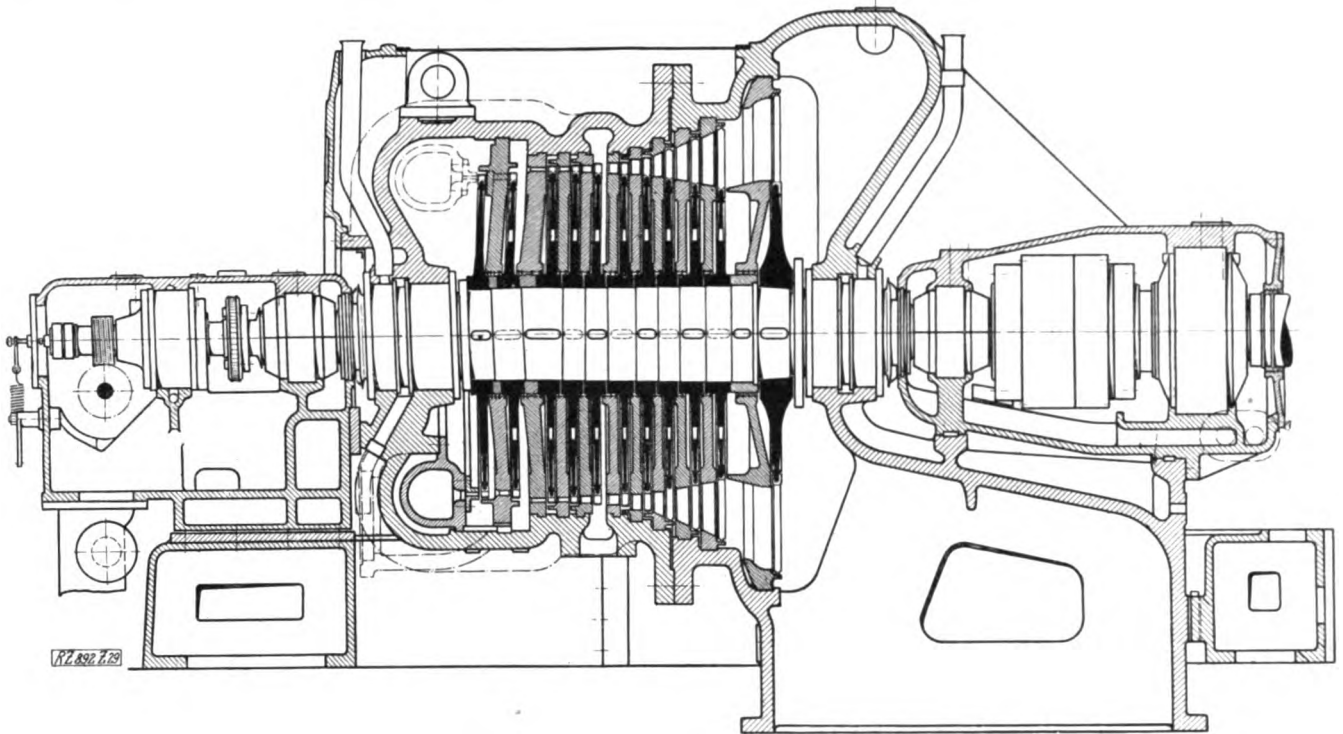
General Electric Co., Ltd., Gleichdruckturbine für 4000 bis 8000 kW und 3000 Uml./min.
